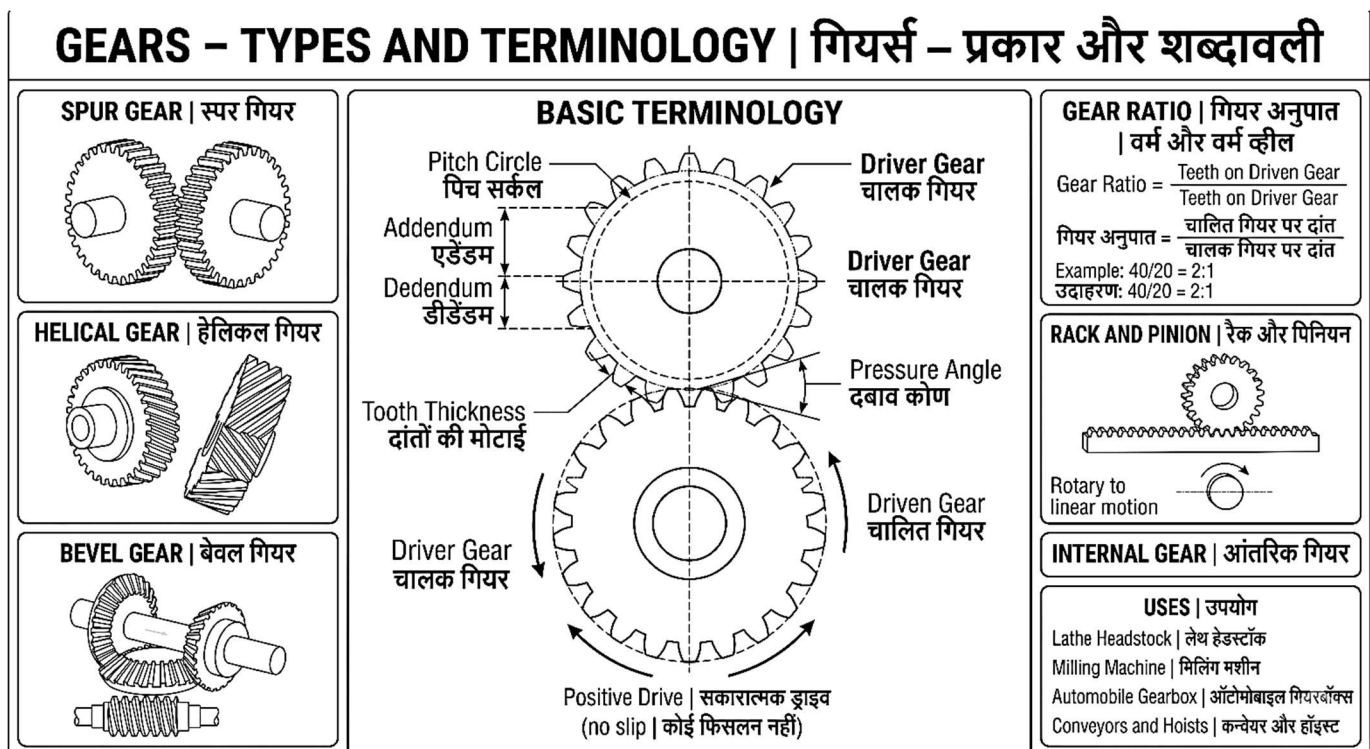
Types of Gears and Gear Terminology | गियर्स के प्रकार एवं गियर शब्दावली
